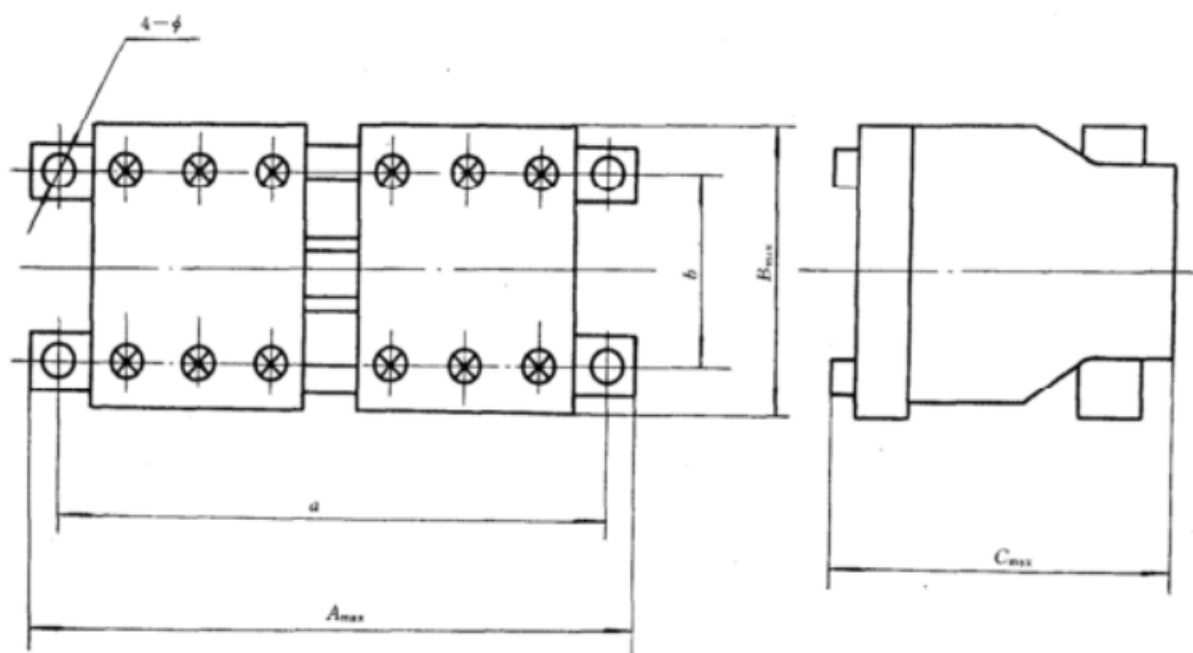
CJX5-120/N、150/N 型联锁接触器外形尺寸与安装尺寸
